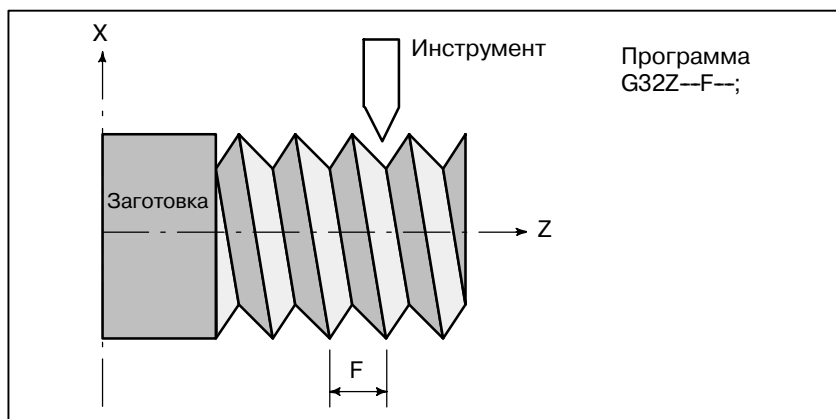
(e) Нарезание цилиндрической резьбы
